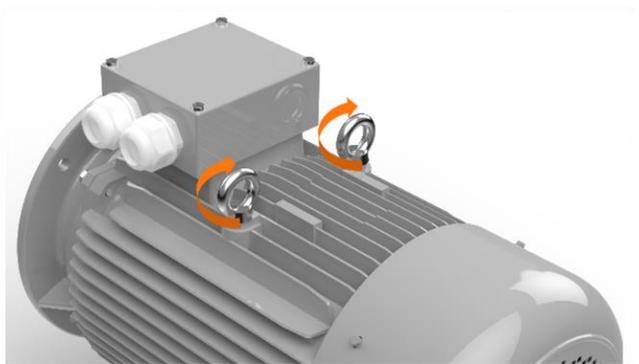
Ringschrauben vor Transport bis zum Anschlag eindrehen
